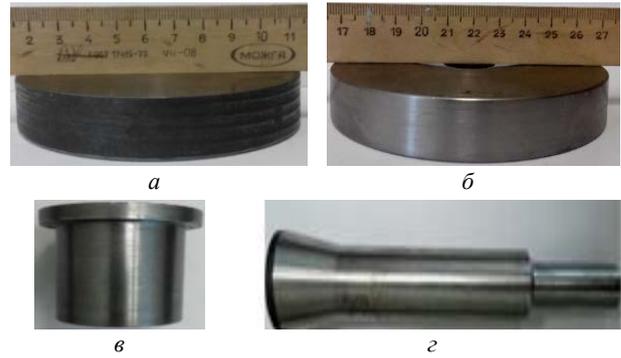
Фотографії деталей штампу для виконання профілювання заготовки: *a* – плита 2, *b* – притискач 3, *в* – кільце 6, *г* – пуансон 7
